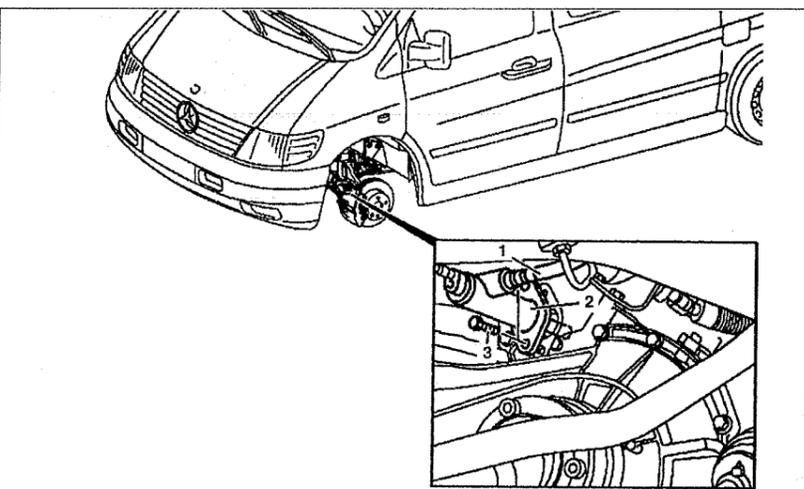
Рабочий цилиндр сцепления (только на автомобилях с двигателями 111.948 и 601.970):
